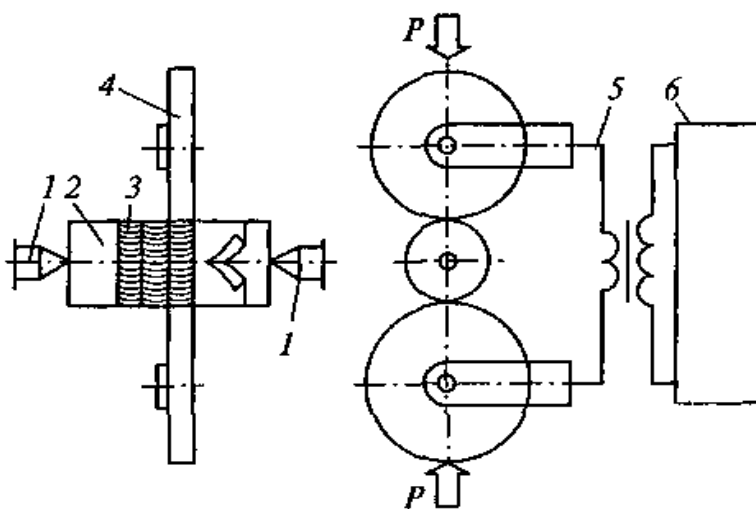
Схема электроконтактной приварки ленты на установке 011-1-02Н: 1-центр; 2-восстанавливаемая деталь; 3-лента; 4-ролик; 5-трансформатор; 6 – прерыватель тока; P-прижимное устройство.
